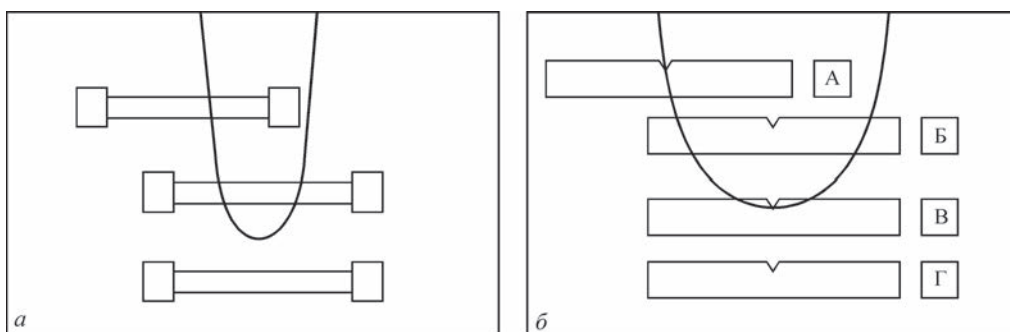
Схема вырезки образцов из сварного соединения стали 15Х1М1ФЛ: а — образцы для испытания на растяжение; б — образцы для испытания на ударный изгиб (А–Г — иллюстрация мест надреза)
